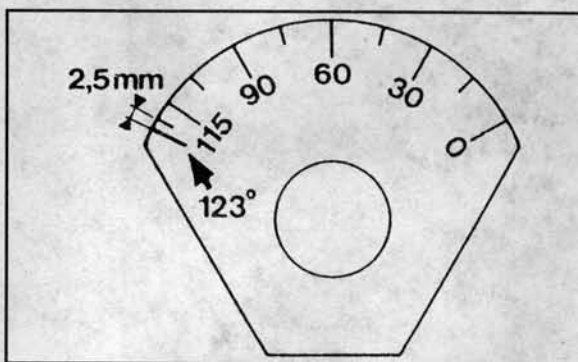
Приспособление 5098 для измерения угла затягивания болтов головки двигателя В172
